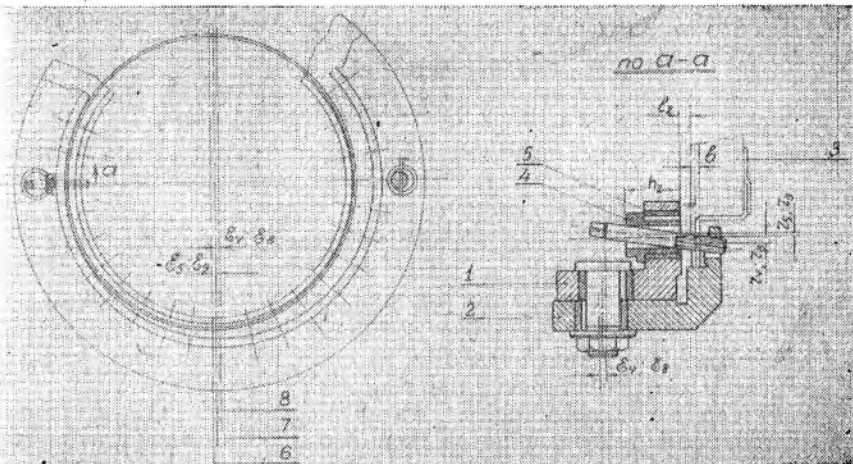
Схема разделки стыковых отверстий в агрегатах
